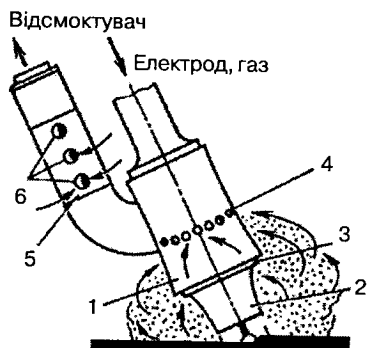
Відсмоктувач для зварювальних автоматів конструкції Airco Welding Products:
